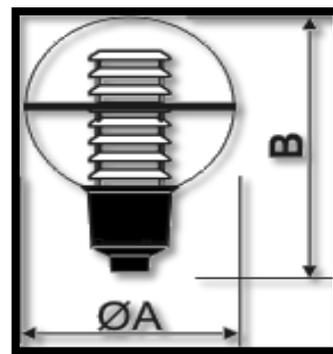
9 Luminaria y Lámpara Led de 35 Watts. Tipo Reflector Arquitectónico para iluminación Fachadas
